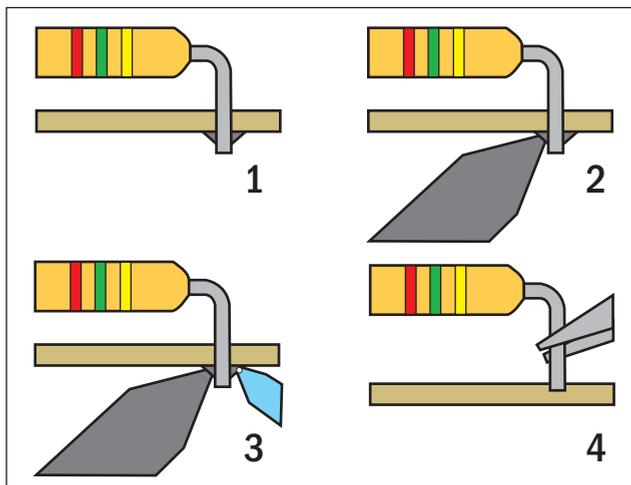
Para desoldar componentes: 1) ubicar los bornes, 2) calentar, 3) aspirar con la pipeta, 4) una vez eliminado el estaño, retirar el componente con una pinza de punta.
